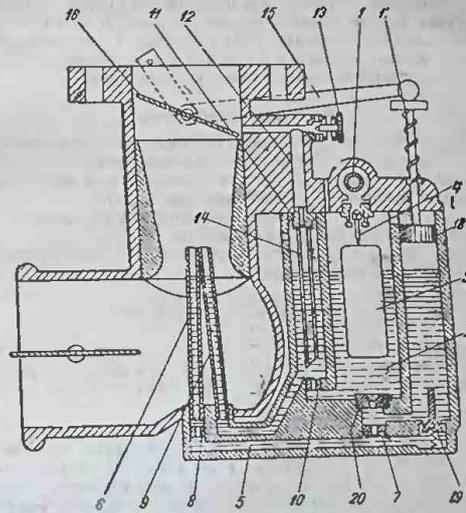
Карбюратор МАЗ-5 (вид со стороны поплавковой камеры)
